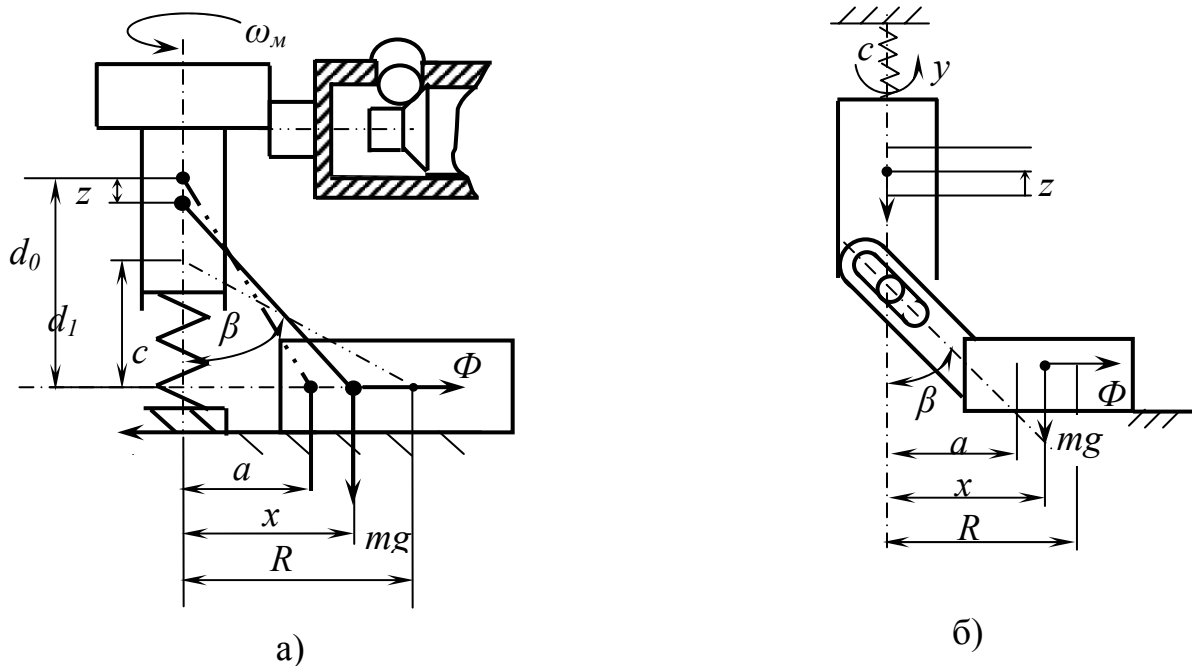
Расчетная схема движения элементов механизмов резьбовозавертывающего инструмента с различным креплением бойков)
